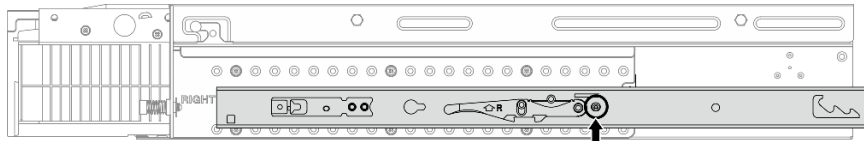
Une vis pour la glissière interne de Kit de glissières avec roulement à billes ThinkEdge 600 mm
